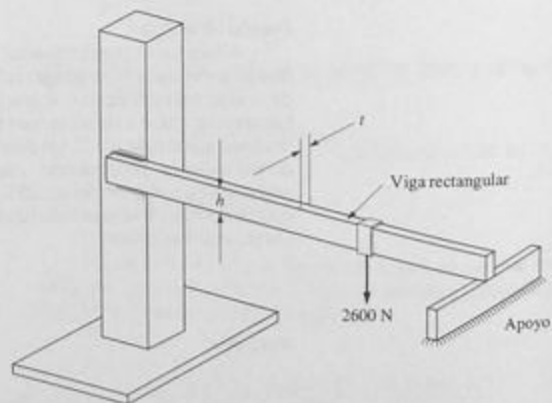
Montaje físico de una viga en voladizo apoyada.
